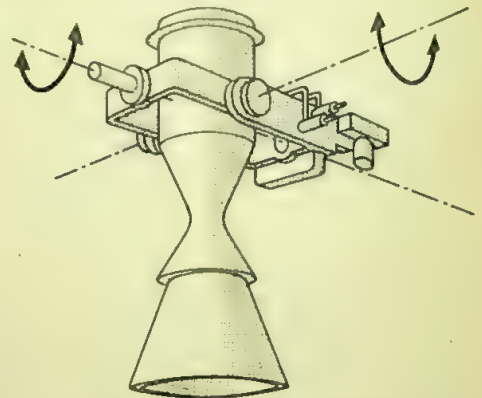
Kardanisch gelagertes Hilfstriebwerk zur Lagesteuerung
